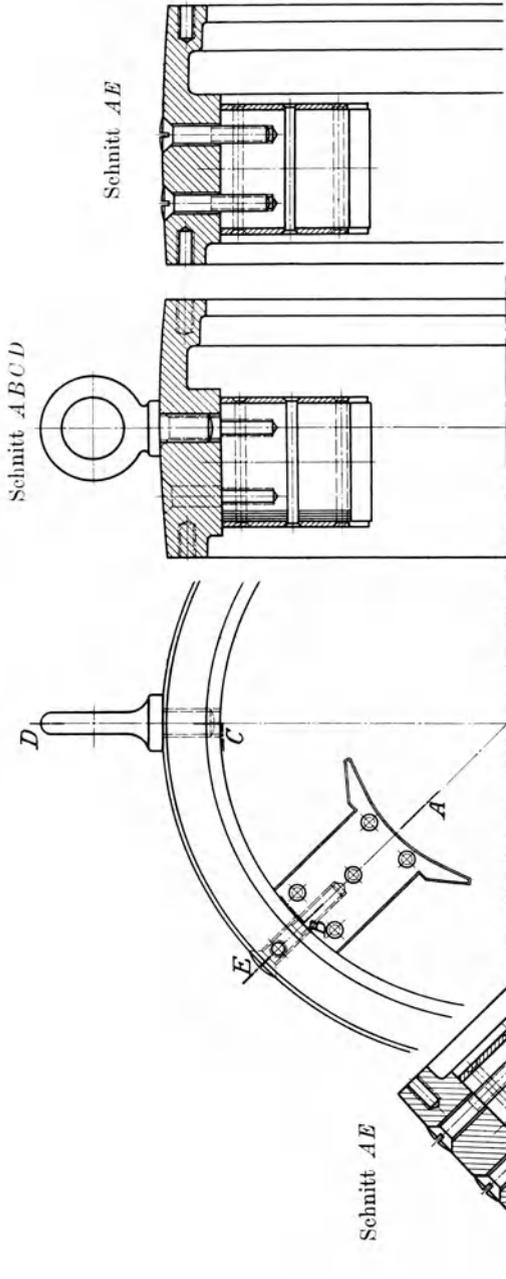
Schräge und in die Bildebene gedrehte Schnitte.
